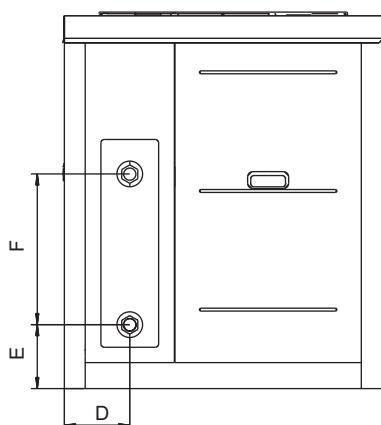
Esboço do desenho cotado do KEM-30 DNS3
